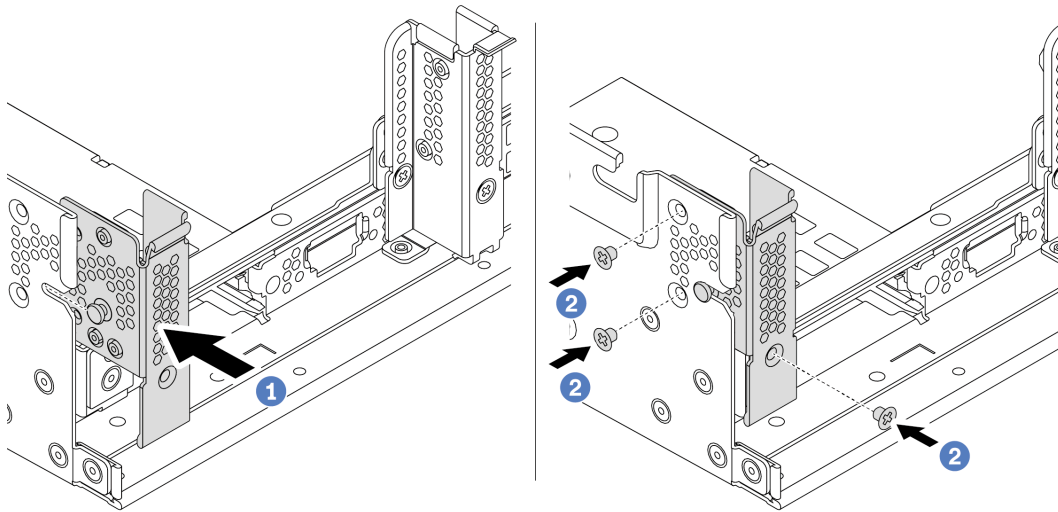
Installazione della staffa posteriore A1 per il montaggio a parete
